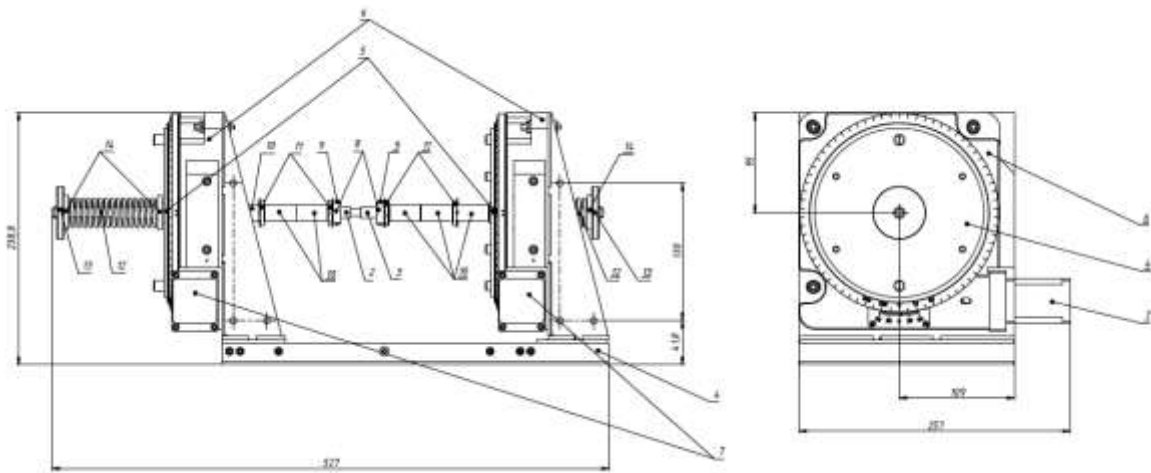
Система закрепления образцов для установки электронно-лучевой сварки стекла
